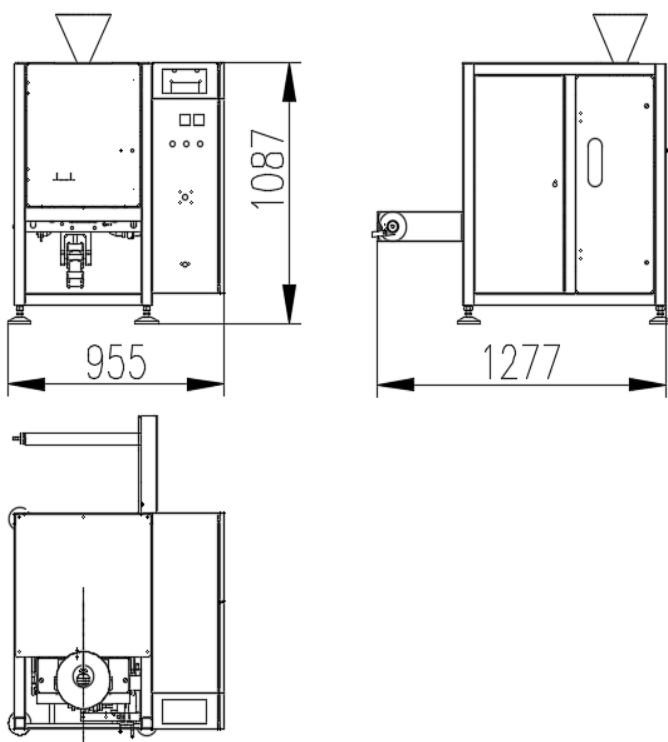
MD420 的外形尺寸 FIG. 2 external dimensions of MD420
